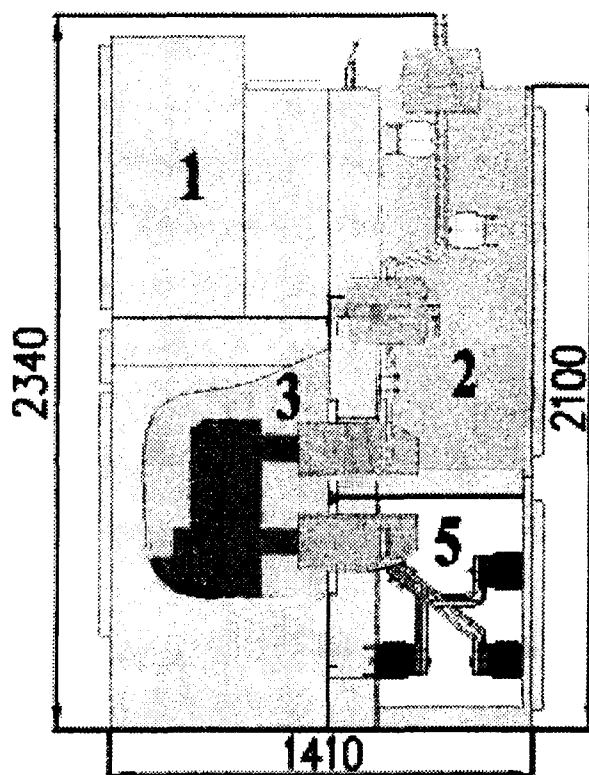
Общий вид и габаритные размеры шкафа К-105
